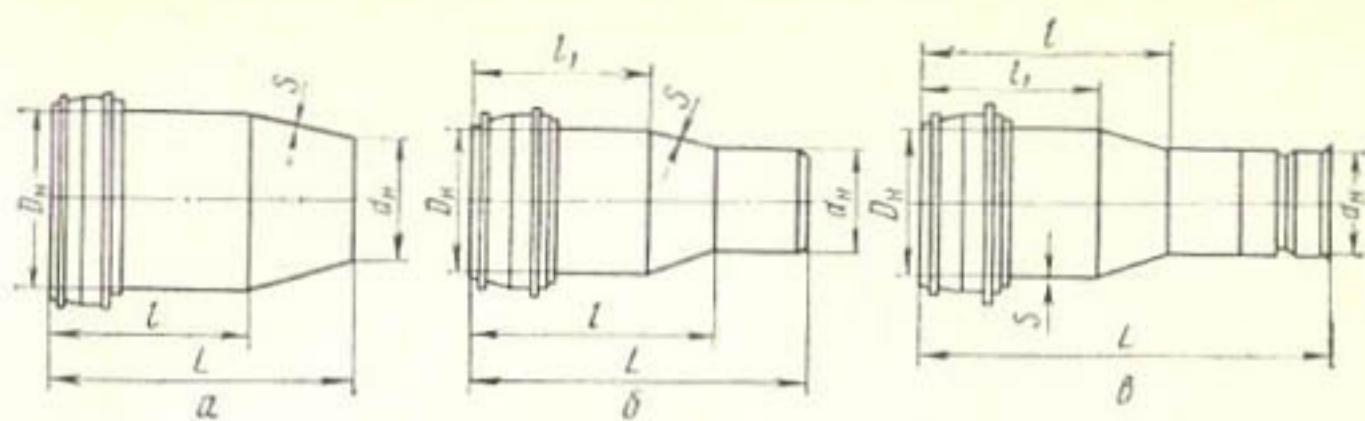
Переходы для соединения железобетонных и металлических труб.
